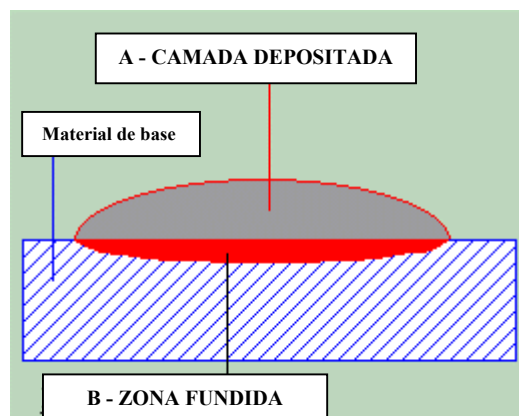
Diluição em uma camada depositada por técnica de soldagem – Adaptada de Marconi, 2002.
